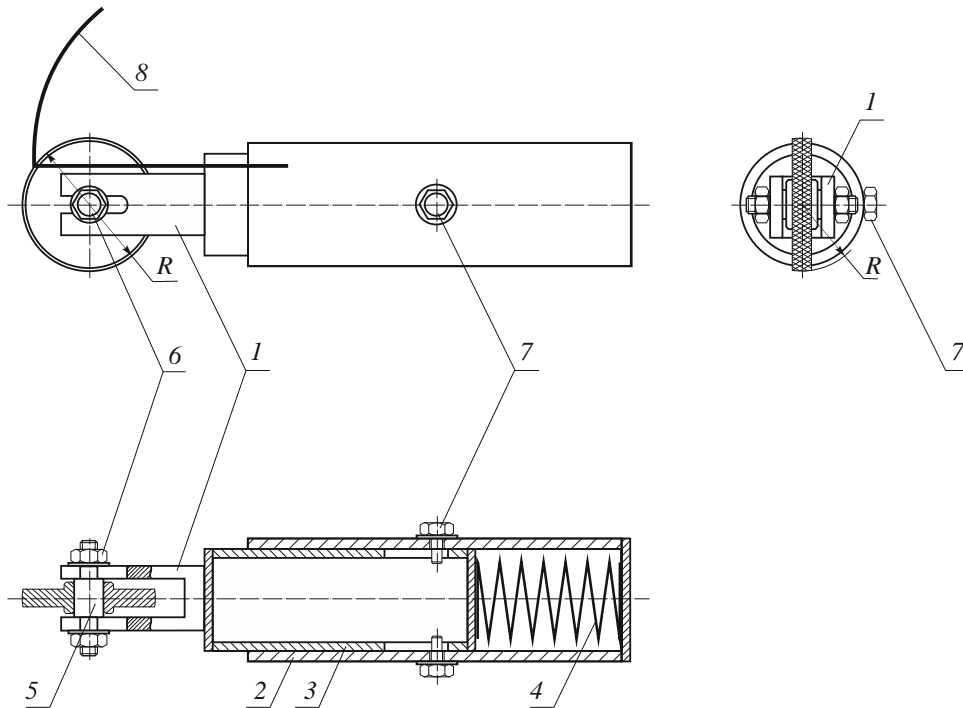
Устройство для смятия верхушек хлопчатника с рифлеными подпружиненными роликами: 1 – вилка телескопической штанги; 2 – внешний стакан; 3 – внутренний стакан; 4 – цилиндрическая пружина сжатия; 5 – ось переменного сечения; 6 – гайка; 7 – специальный болт; 8 – кустонаправитель
